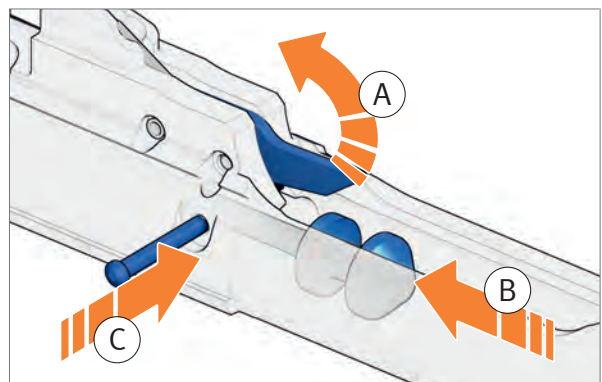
Haltebolzen in den Verschlusssträger drücken
